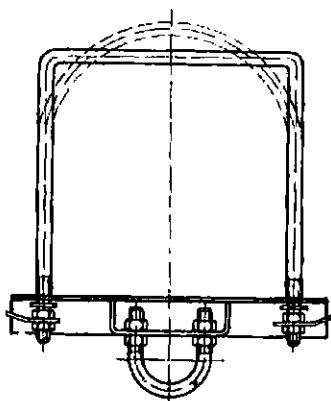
Ansamblu de prindere pe stîlp cu brățară.
